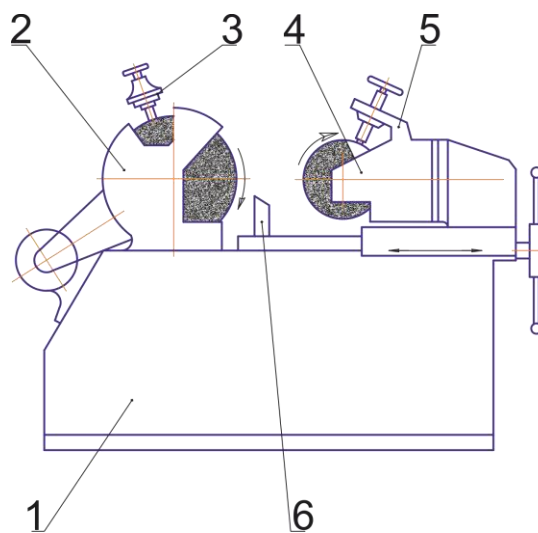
Безцентрово-шліфувальний верстат: 1 – станина; 2 – бабка з шліфувальним кругом; 3 і 5 – механізм для правлення круга; 4 – бабка з веденим кругом; 6 – підтримуючий ніж.
